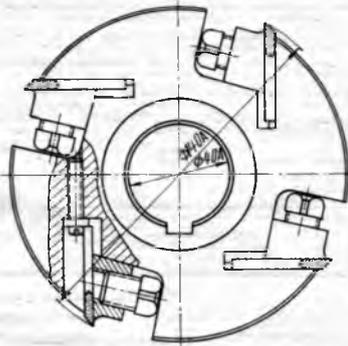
Цилиндрическая сборная фреза с ножами, армированными твердым сплавом ВК10
